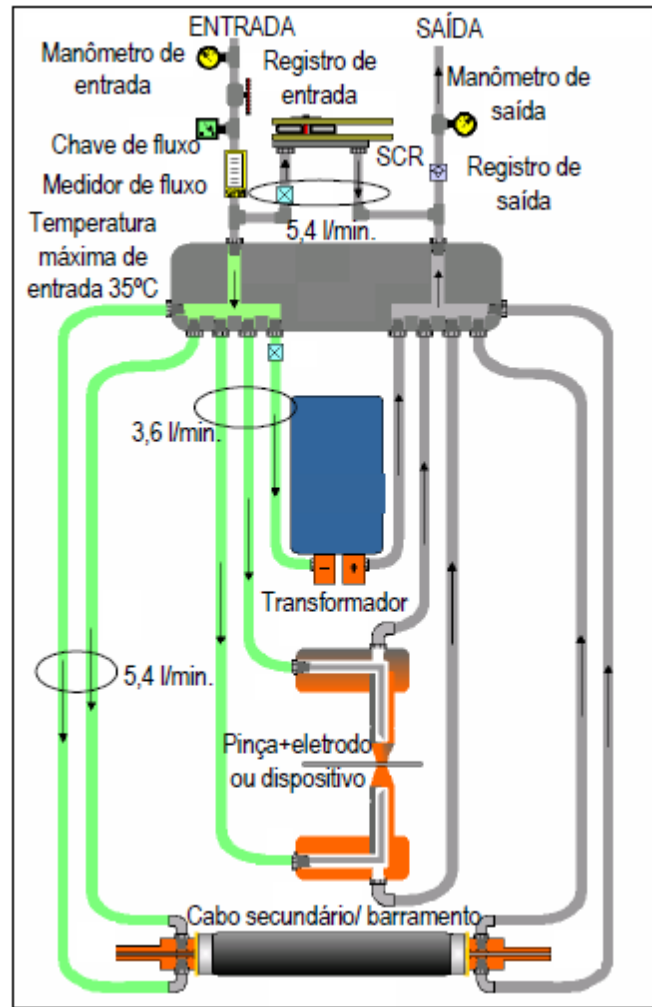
Sistema de Refrigeração do Processo de Soldagem
